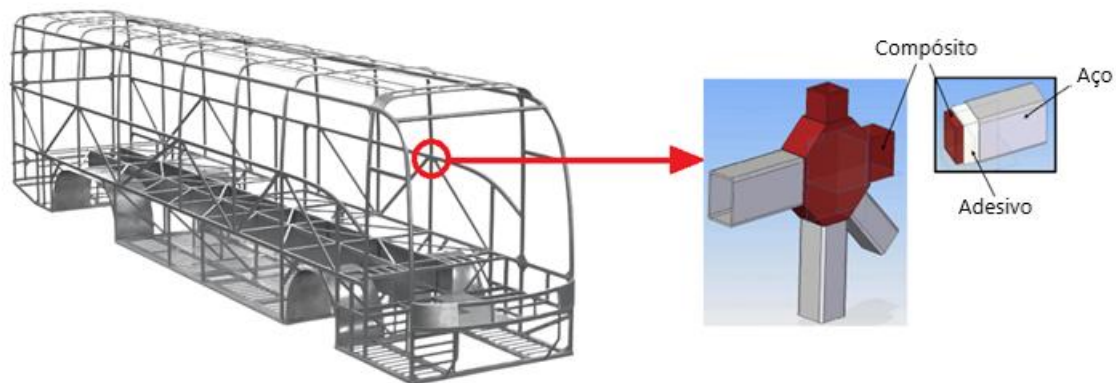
Junta adesiva tubular aplicada na estrutura de um autocarro [77]
